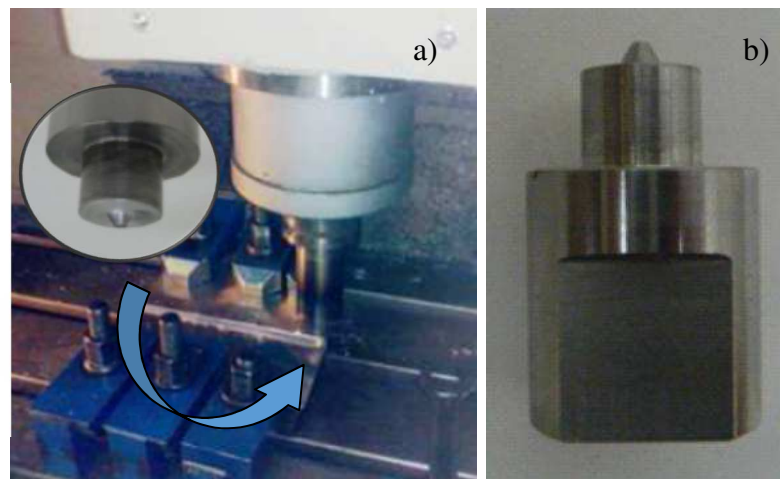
a) Particolare del processo di saldatura FSW al CNC e b) utensile per le prove di FSW
